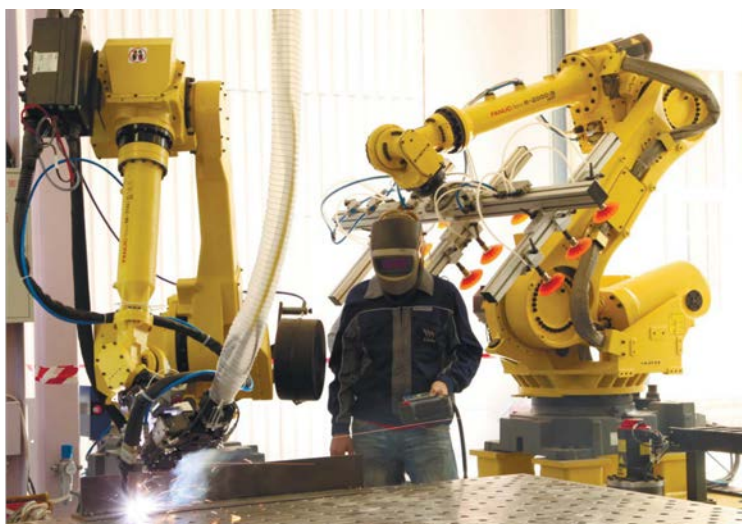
Роботизированный комплекс для лазерной резки и сварки металлоконструкций для морских и речных судов
